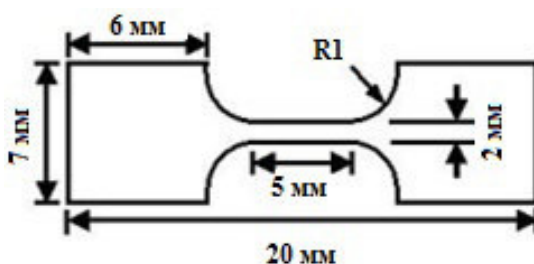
Типичный образец, изготовленный методом ЭЛС
